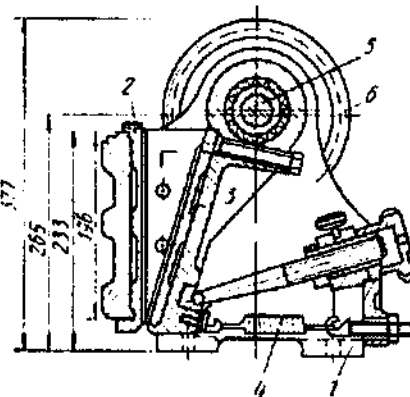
Щековая дробилка ДЦ-100×60: 1 — станция; 2 — неподвижная щека; 3 — подвижная щека; 4 — пружины; 5 — шатун; 6 — маховик
